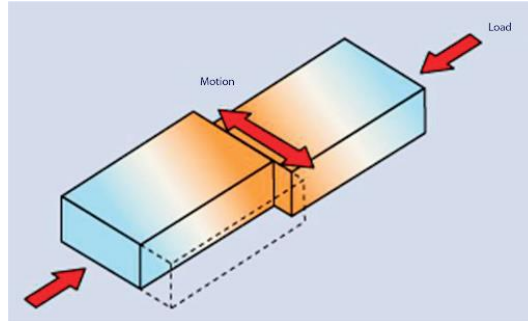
Esquema de Funcionamiento de una Soldadura LFW
